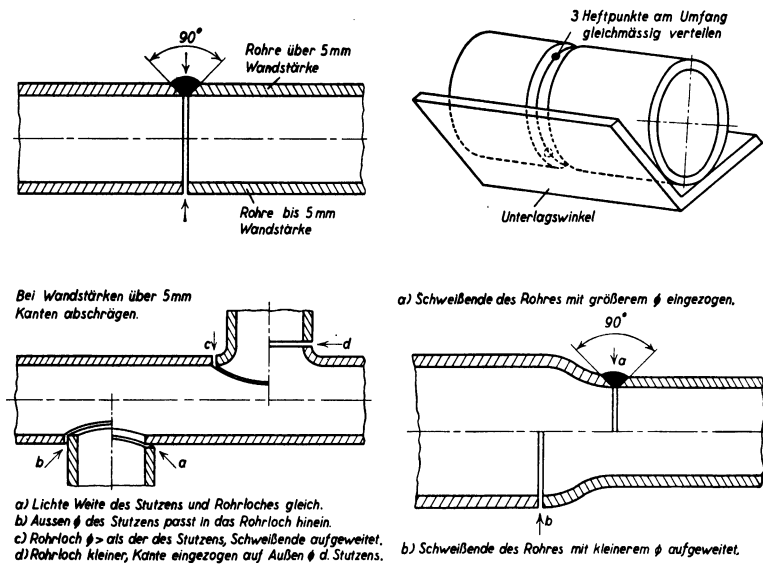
Rohrverbindungen durch Schweißen.
